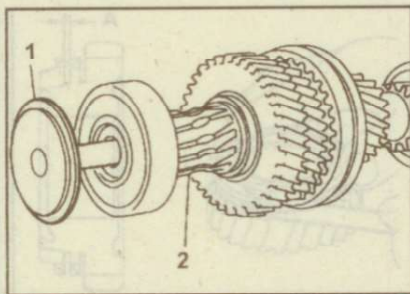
Снятие канала для смазки (1) с заднего подшипника первичного вала (2)
